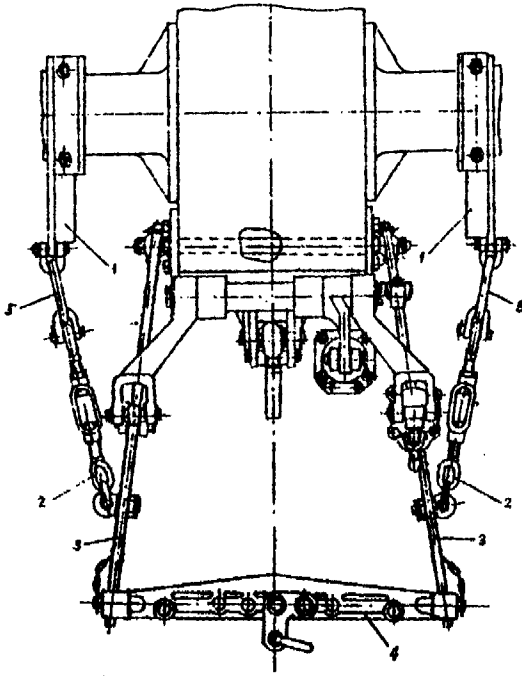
Навесное устройство с наружными стяжками: 1 – кронштейн; 2 – стяжка; 3 – продольная тяга; 4 – поперечина; 5 – кольцо стяжки
